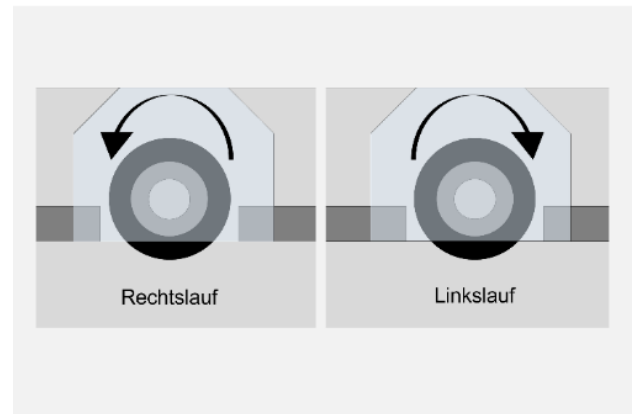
Skizze mit Draufsicht auf Spindel
